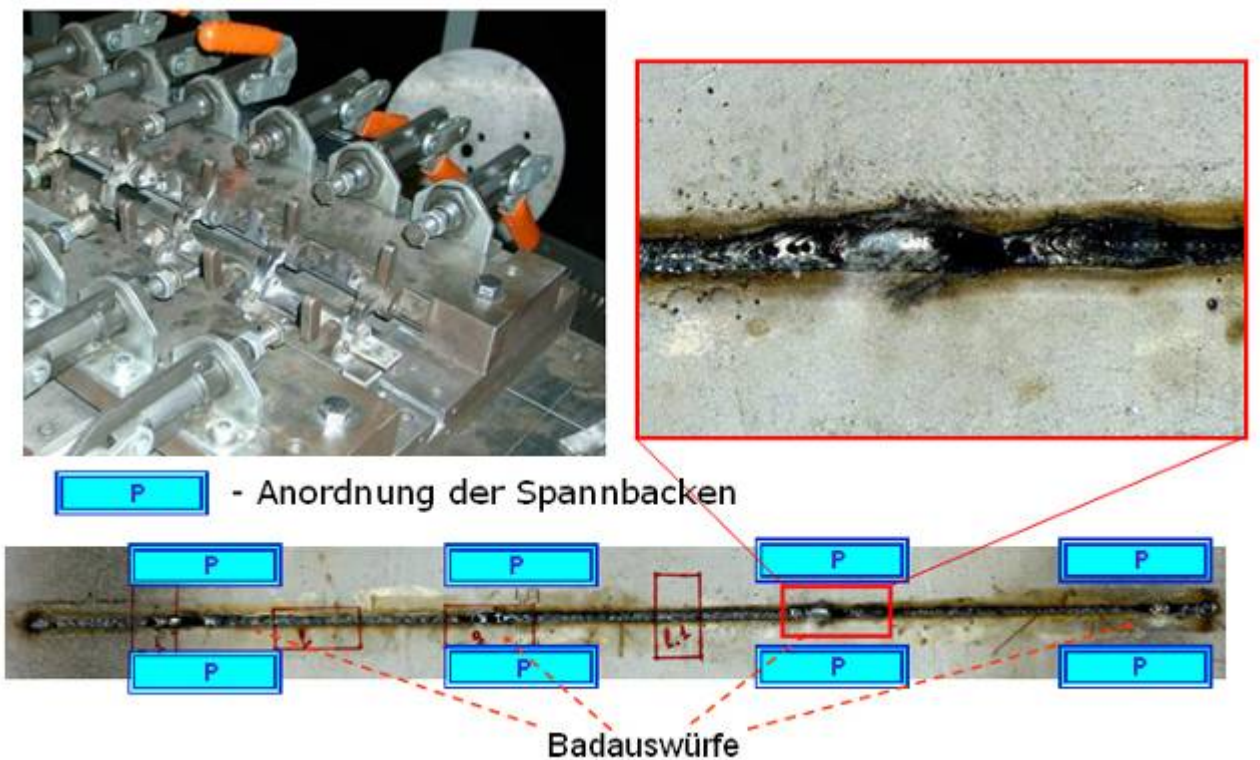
Einzelne rechteckenförmige Spannbacken (acht Spannelemente)
